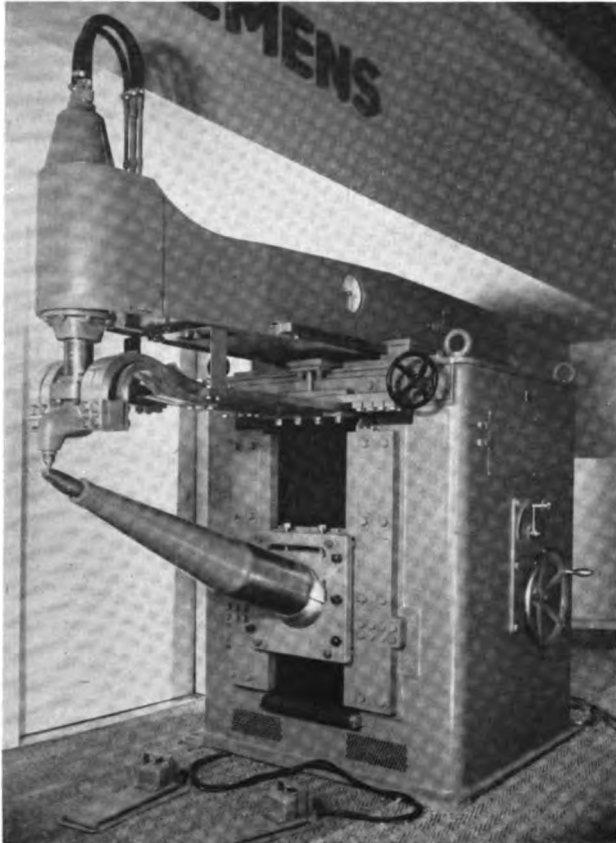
Leichtmetall-Schweißmaschine WP 82
